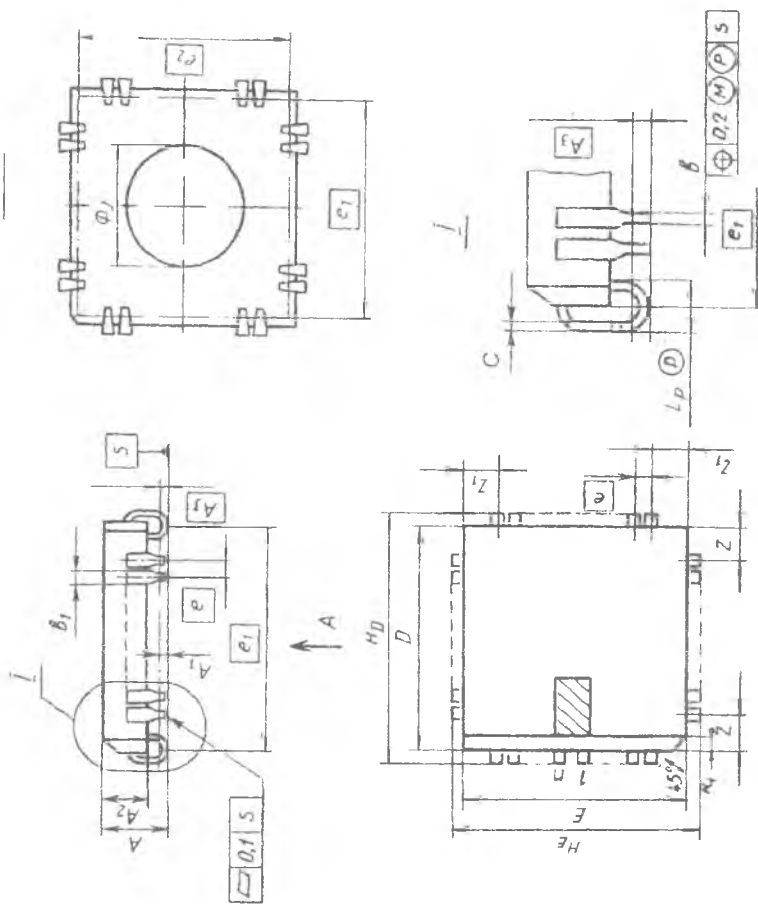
Конструкция корпуса типа 4 подтипа 5
